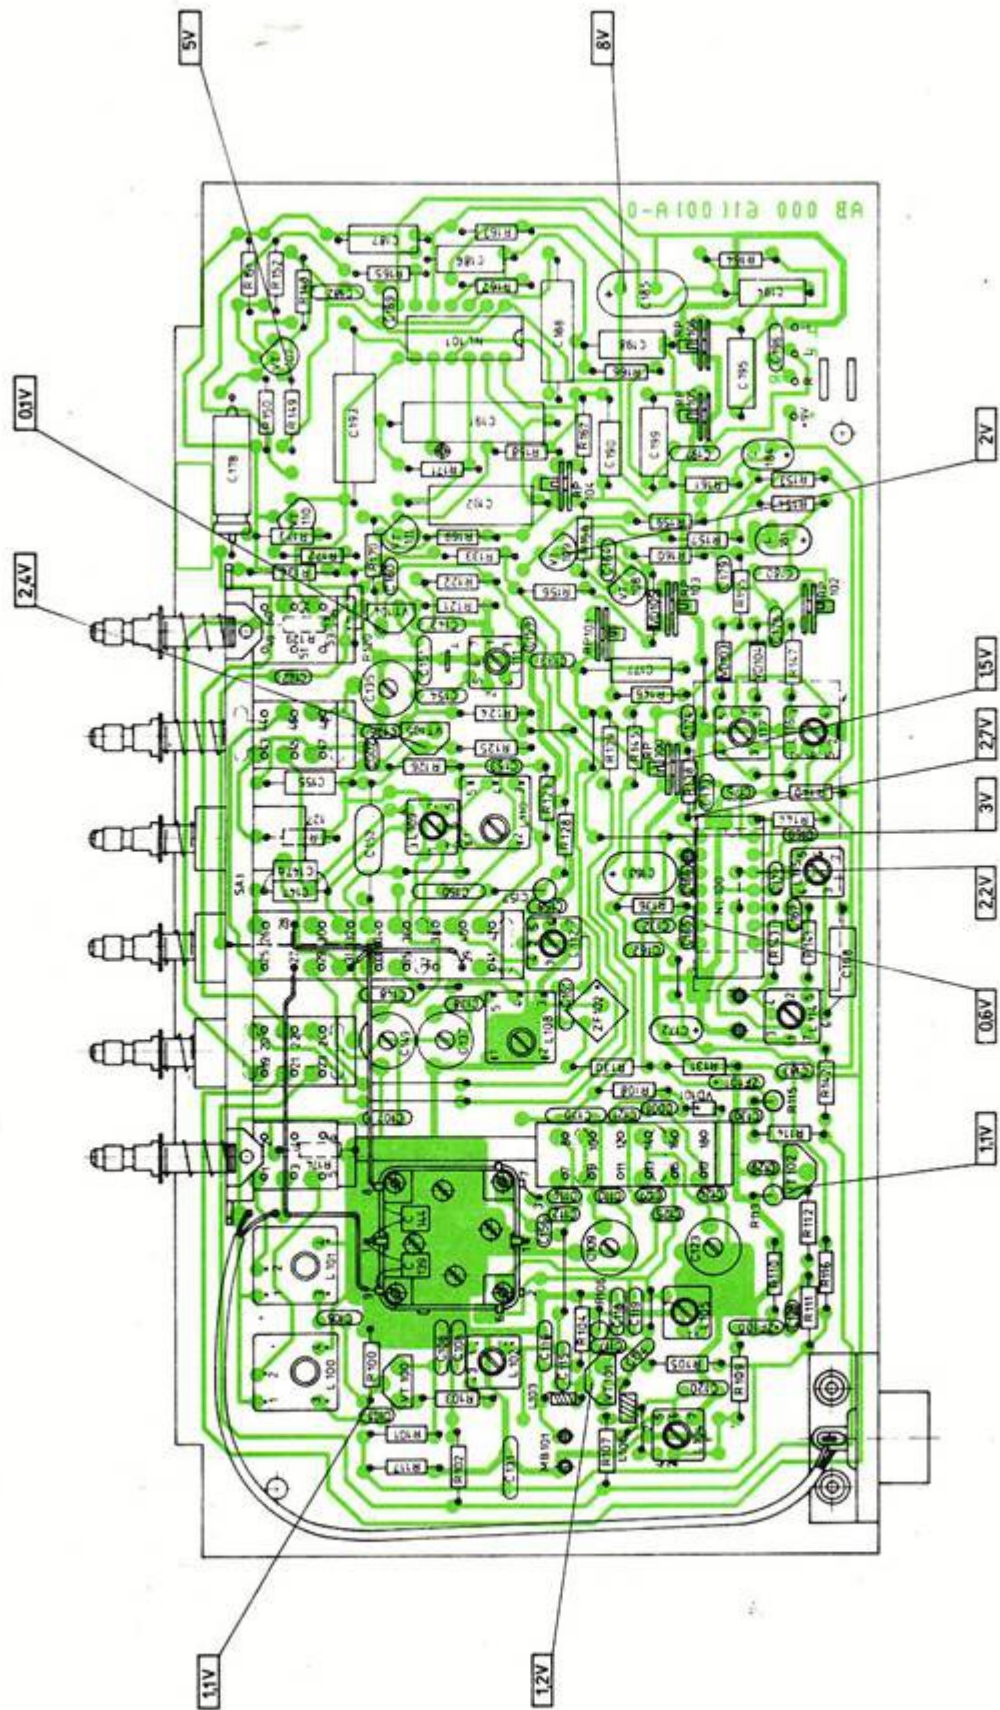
D7 - płytki elektronicznej sterującej funkcjami mechanizmu - widok od strony elementów
